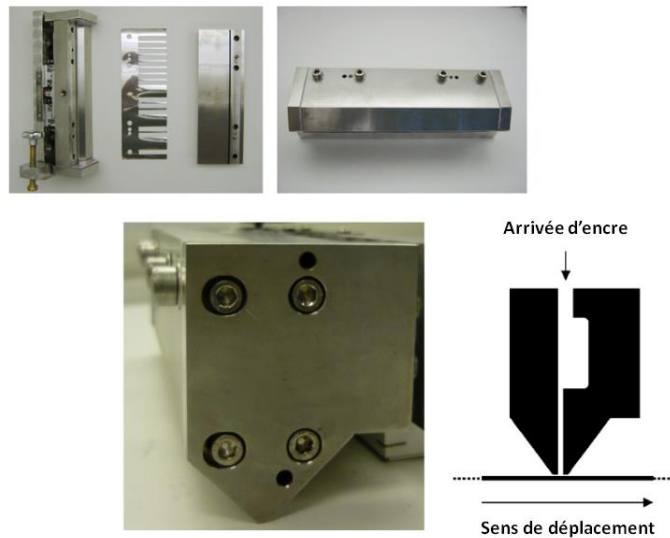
Photographies décrivant la tête du slot-die : les deux parties à assembler et le masque entre les deux (en haut à gauche), la tête assemblée vue du dessous (en haut à droite), la tête assemblée vue du côté (en bas à gauche). Schéma du principe du slot-die en bas à droite [51]
